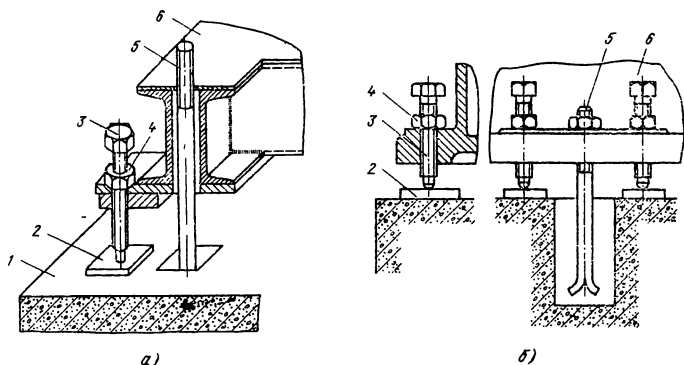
Применение регулировочных винтов для установки сварных (а) и литых (б) конструкций:
